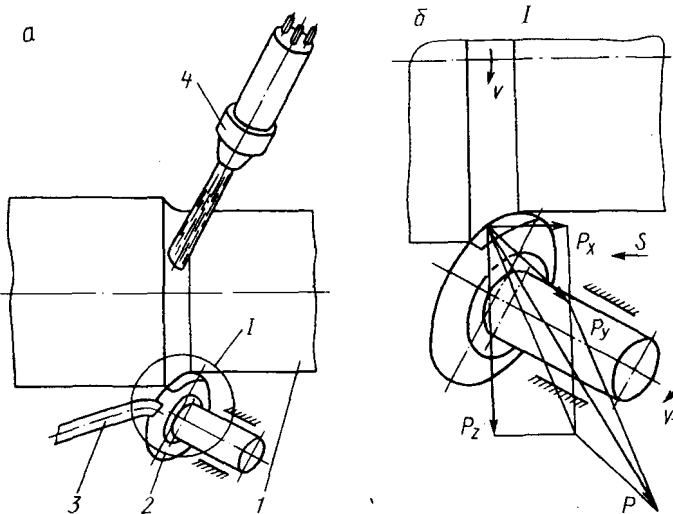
Схема обработки детали вращающимся инструментом (а) и схема действия сил резания (б): 1 — обрабатываемая деталь; 2 — вращающийся инструмент; 3 — подача смазки, охлаждения; 4 — источник нагрева
